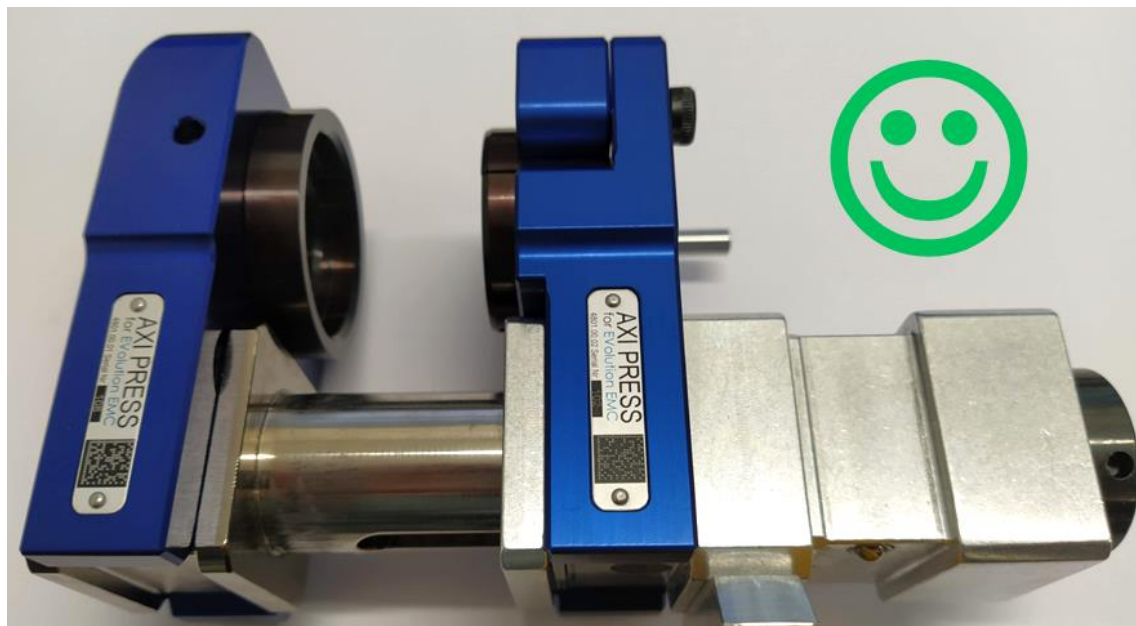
Gli attrezzi montati sull'utensile AXI PRESS (variante 1): attrezzo di serraggio nella posizione di inserimento 1, attrezzo di flangiatura nella posizione di inserimento 2
